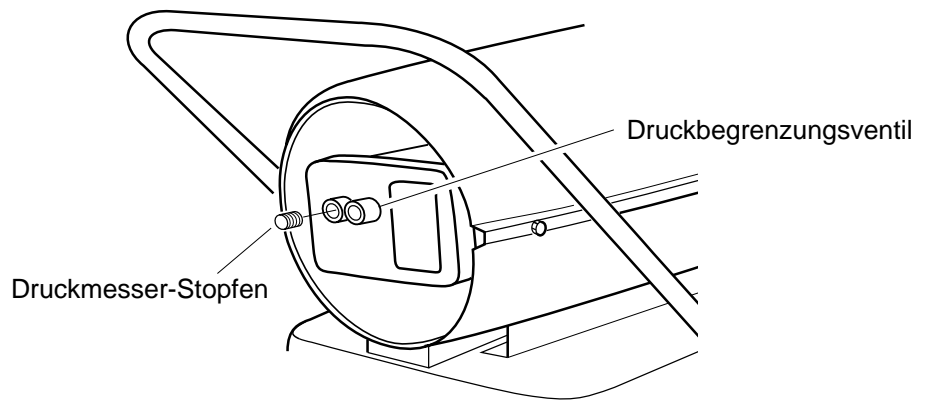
Entfernen des Druckmesser-Stopfens
